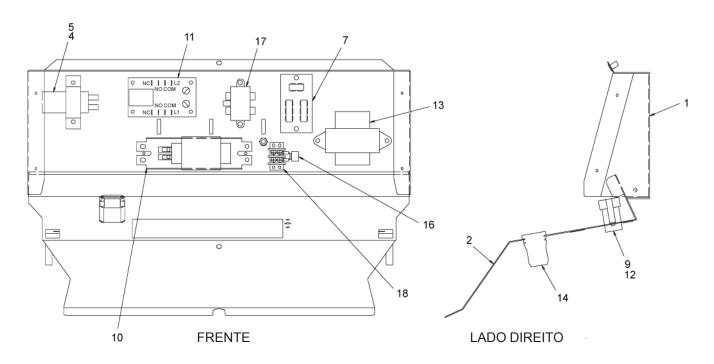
VISÃO EXPLODIDA DA COMPOSIÇÃO DA CAIXA ELÉTRICA
